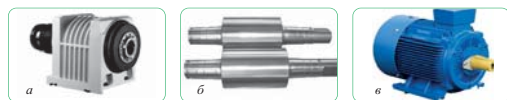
а – шпиндель токарного станка; б – валки в прокатном стане; в – электродвигатель
